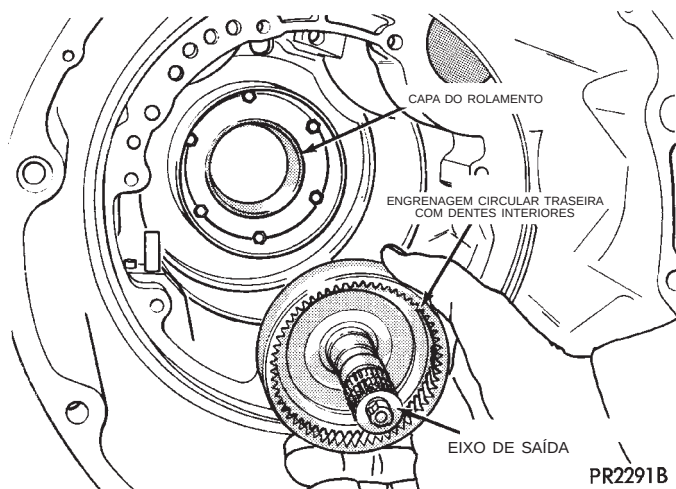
Remoção do Eixo de Saída e do Conjunto de Engrenagem Traseira Circular com Dentes Interiores
